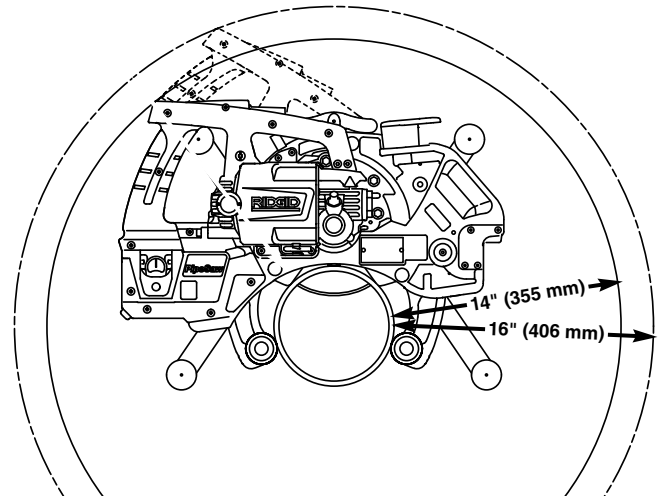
B – Encombrement radial de la PipeSaw sur tuyau
